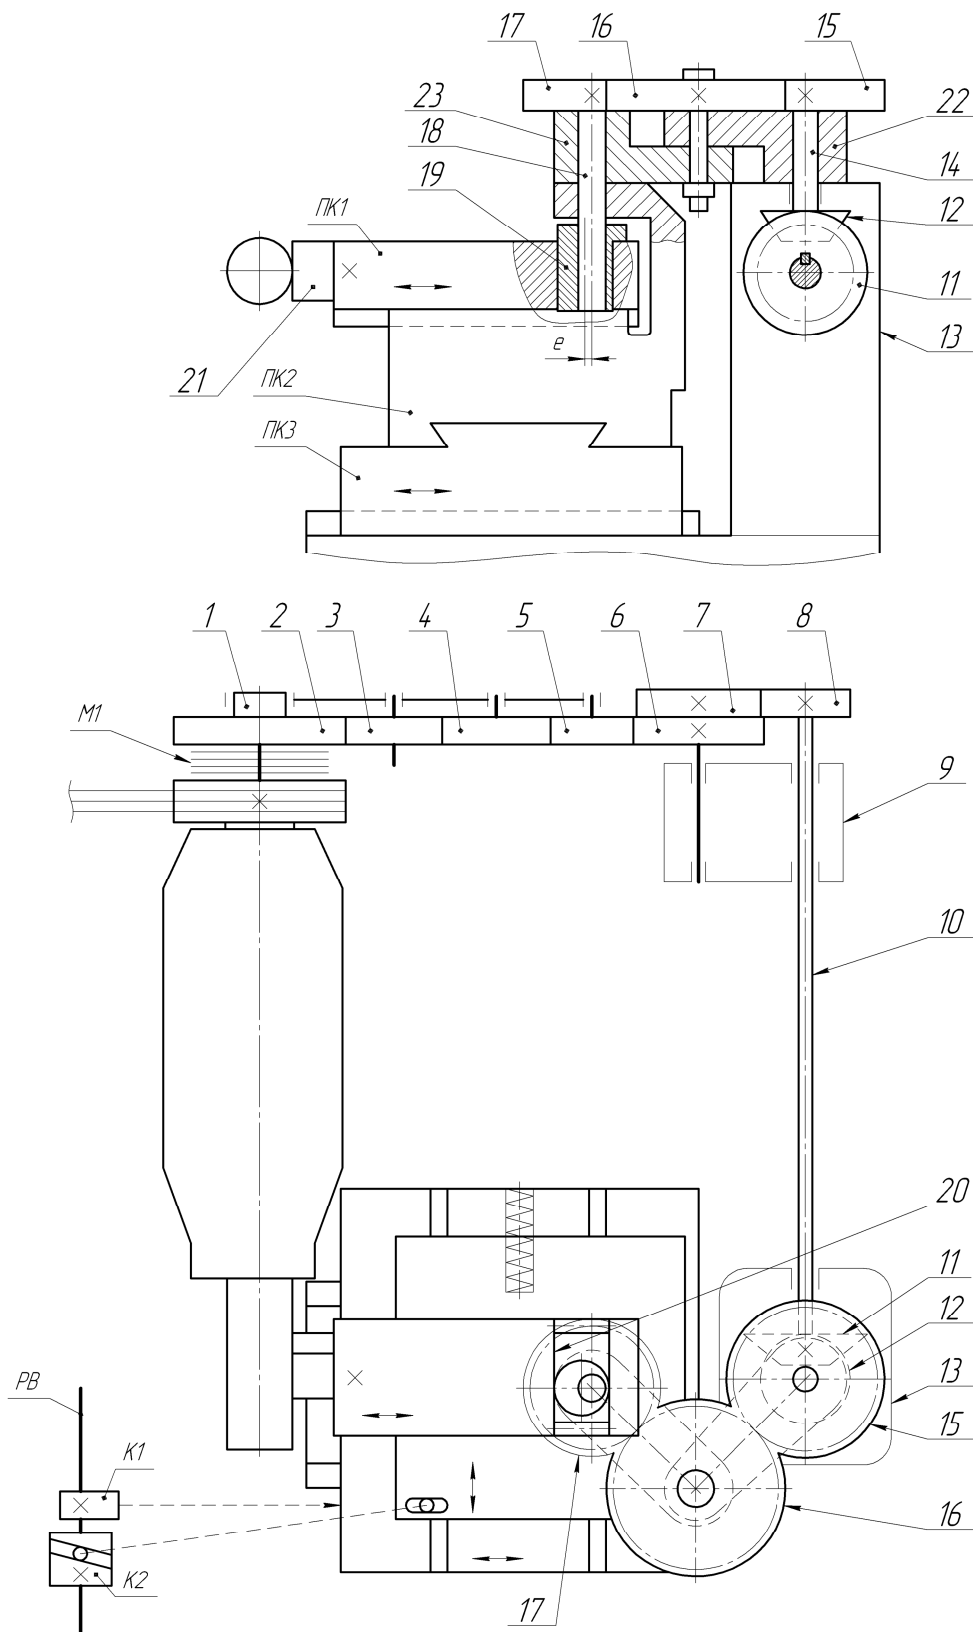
Кинематическая схема дополнительного устройства к ТРА для обработки наружных РК-профильных поверхностей методом косоугольного точения безвершинным резцом
